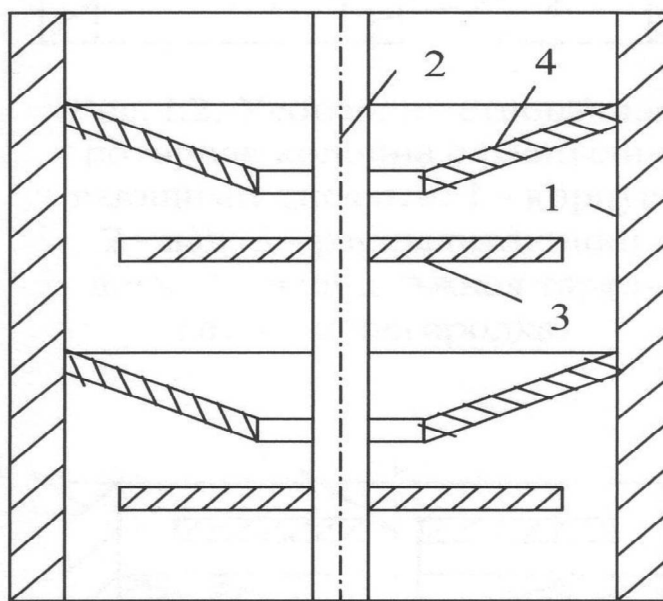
Роторная колонна с распиливающими дисками: 1 - корпус; 2 - вал; 3 - распиливающий диск; 4 - неподвижная тарелка.
